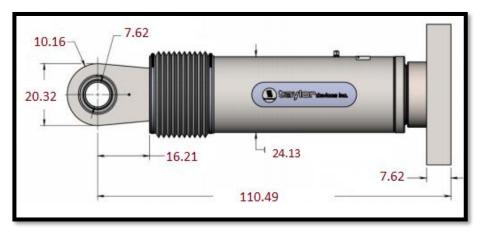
Dimensiones del disipador de 330 kip. Fuente: Propia
